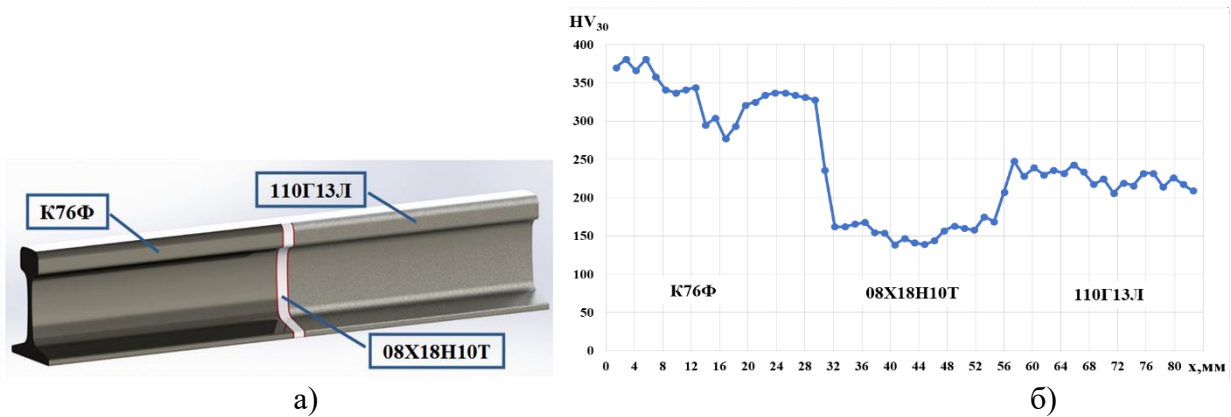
Схема комбінованого з'єднання (а), розподіл твердості у зварній хрестовині із сталей К76Ф/08X18Н10Т/110Г13Л (б)
